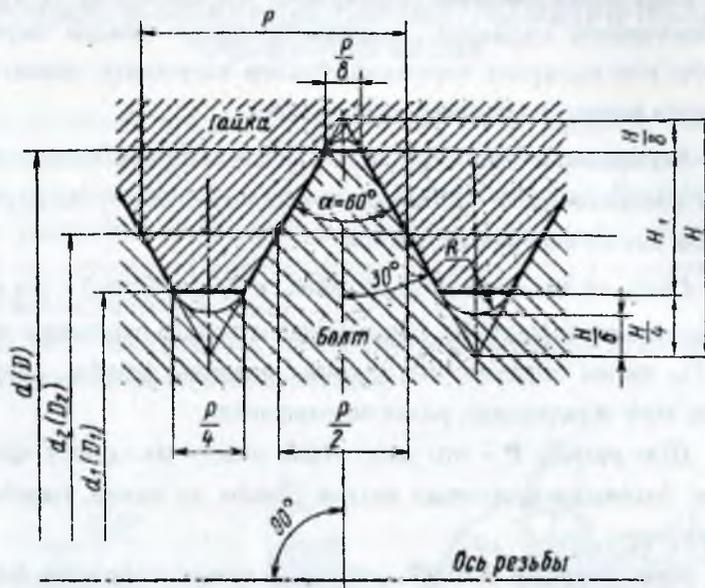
Профиль и параметры метрической крепёжной резьбы
